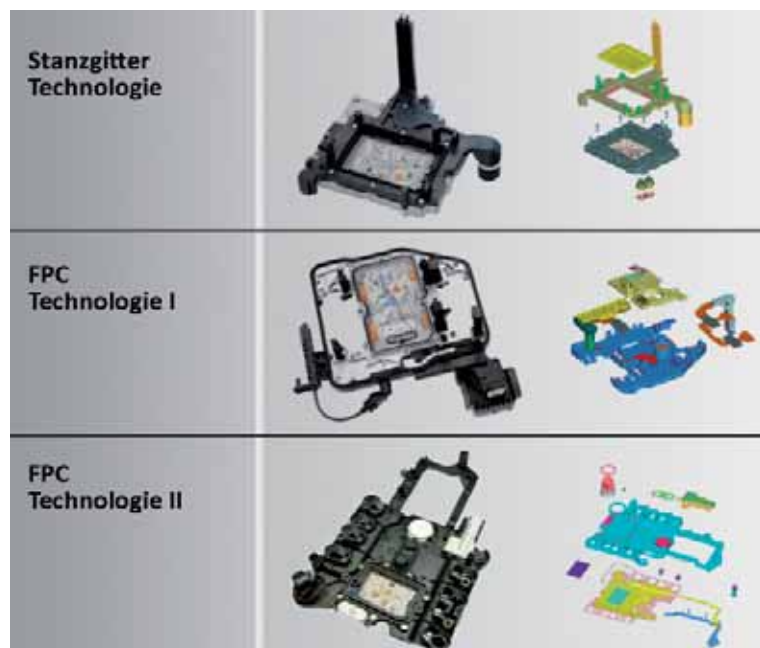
Mechanik-Plattformen zur Realisierung von integrierten Getriebesteuerungen
